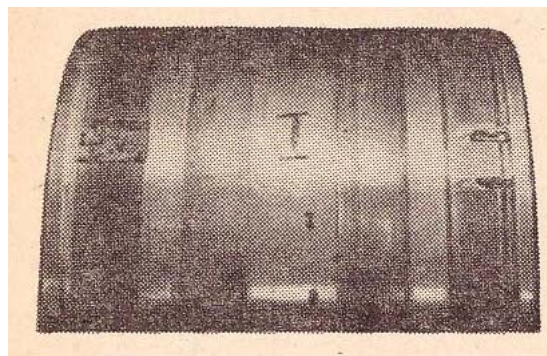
Вид изношенной дорожки внутреннего кольца беспараторного роликоподшипника [7]
